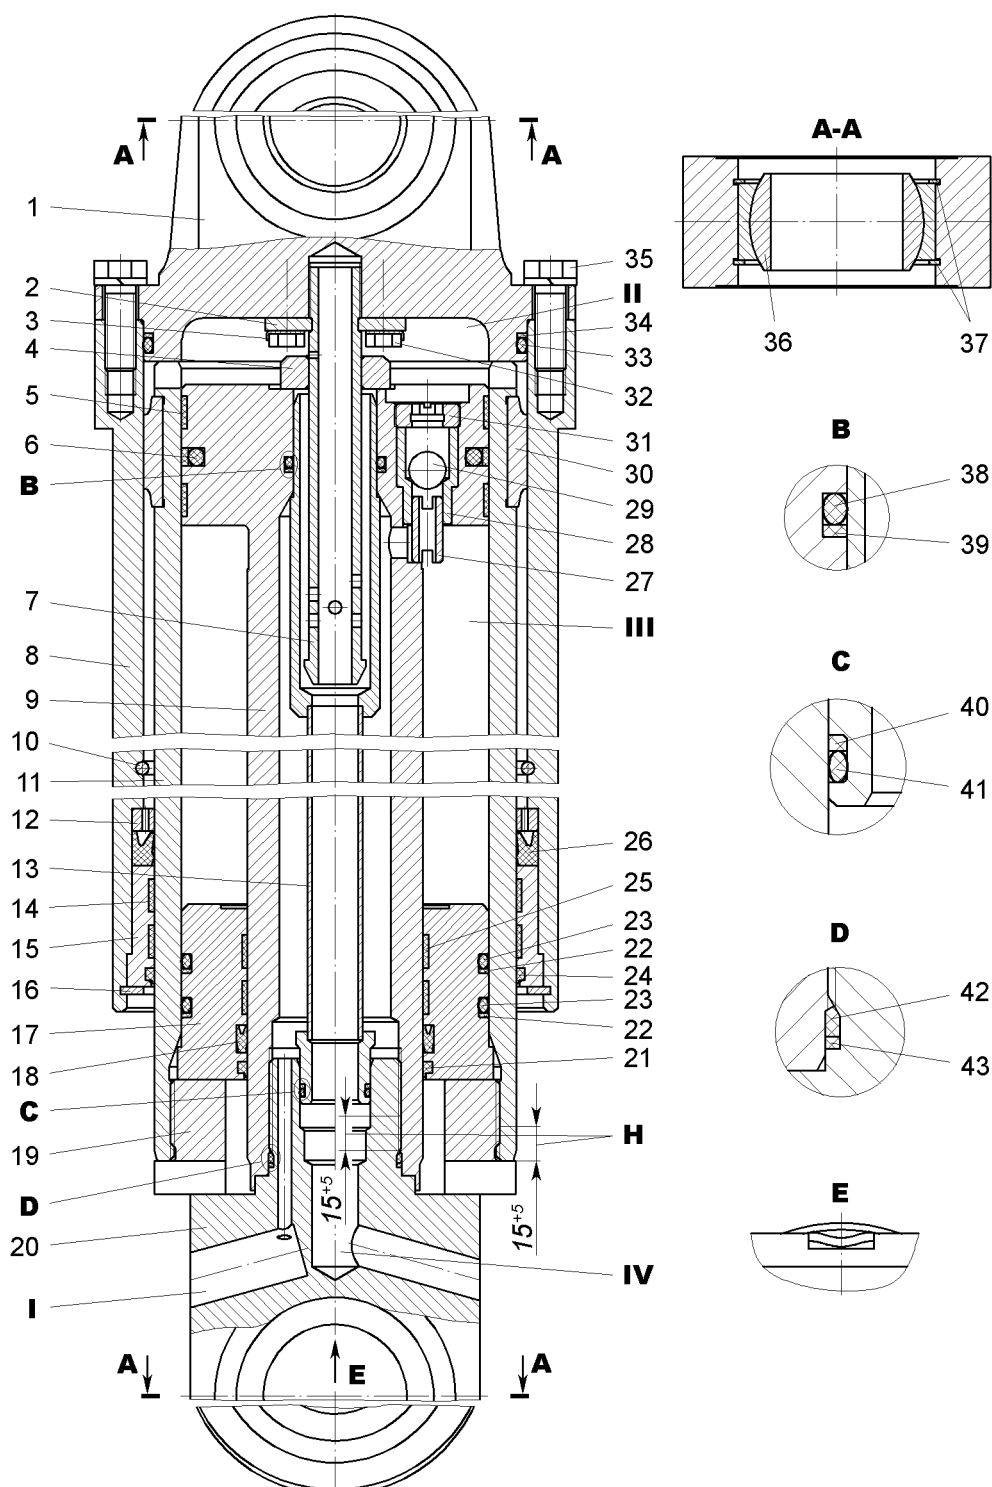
Цилиндр опрокидывающего механизма:
